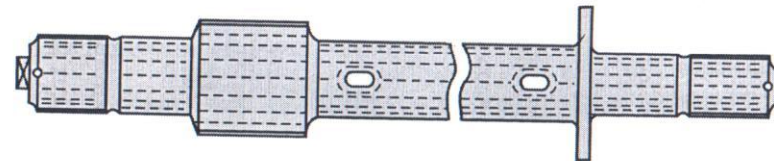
Контроль цилиндрических поверхностей тяги поводка
